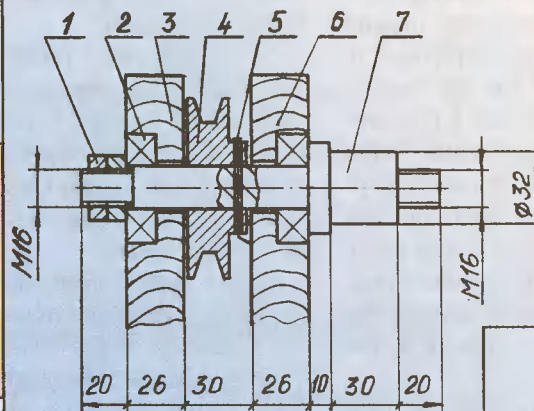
Вал в сборе со шкивом: 1 - контргайка М16; 2 - подшипник №206; 3, 6 - стойки; 4 - шкив; 5 - шпилька Ø4 мм; 7 - вал.
